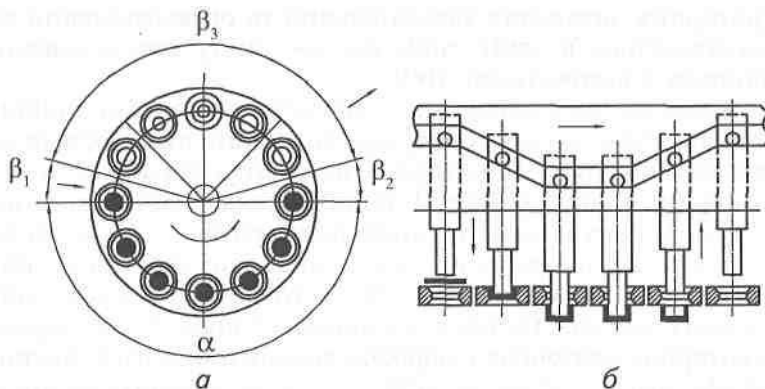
Роторний автомат для виготовлення ковпачків: а — робоча і допоміжна зони; б — розгортка робочої зони ротора
